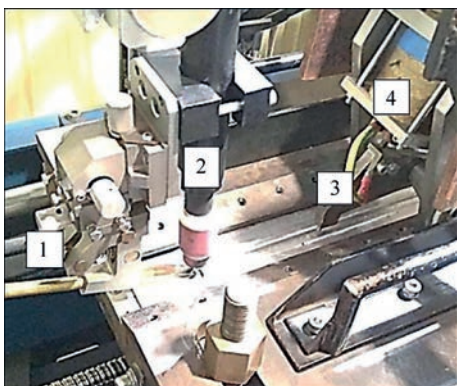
Апаратний комплекс для автоматичного зварювання ТІГ, яке є сумісним із ЕДО зварного шва: 1 – система для подання присадного дроту; 2 – пальник для зварювання; 3 – електродний пристрій; 4 – лінійний соленоїд переміщення електроду ЕДО
